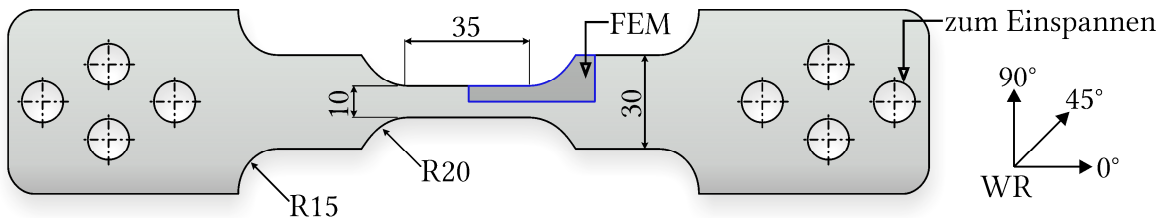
Probenabmessungen und -entnahmerichtungen für die Flachzugversuche; die Bohrungen sind zum Durchstecken der Befestigungsschrauben, damit die Probe zwischen zwei Werkzeugen flächig eingespannt wird (Kerbwirkung vermeiden)
